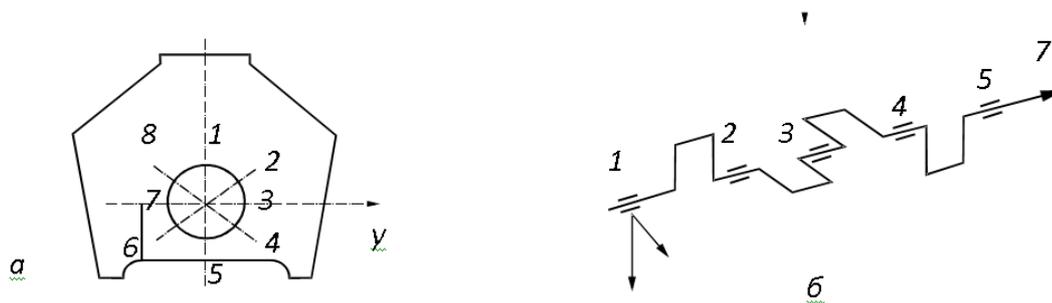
Схема измерений биения коренных шеек: а – вид сбоку корпуса; б – схема расположения коренных шеек колен; 1 ... 8 – фиксированные точки измерений коренных опор в плоскостях поперечного сечения; 1...5 – номера коренных шеек
